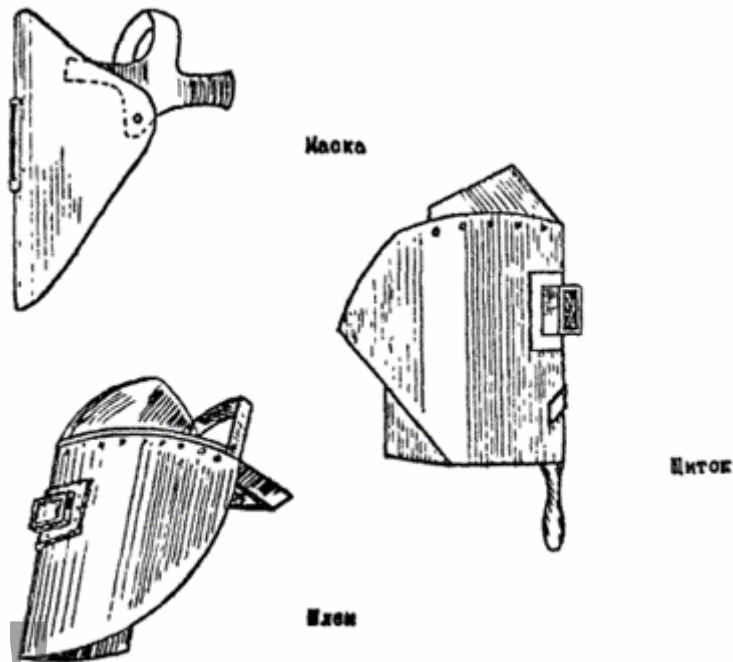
Средства защиты от воздействия сварочной дуги и брызг металла
